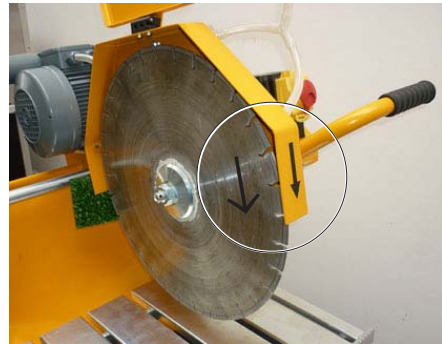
, Алмазный диск смонтирован, направление вращения режущего вала и режущего диска
